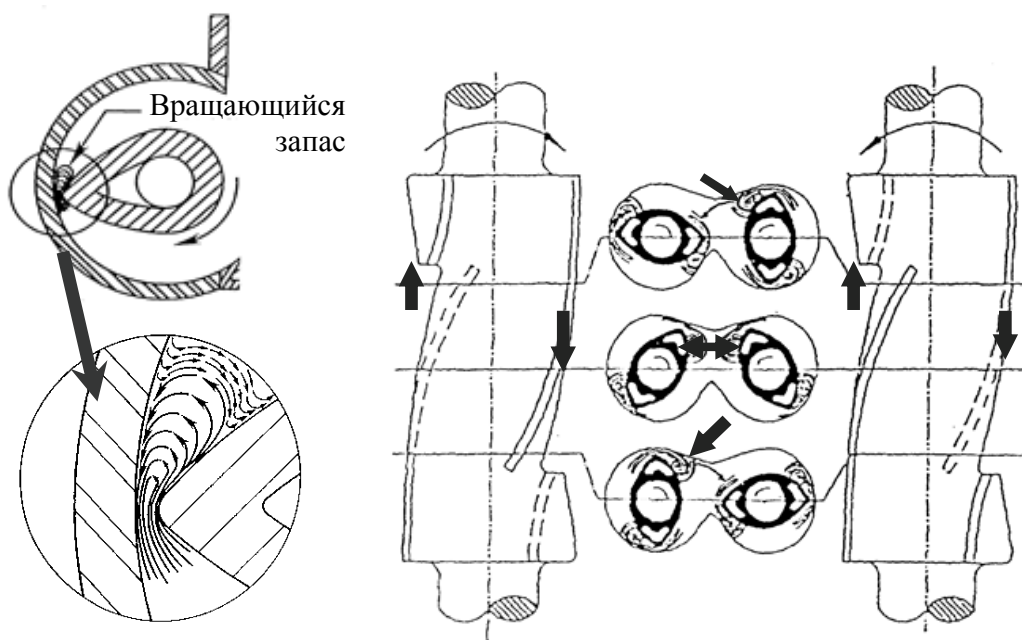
Схема обработки материала в резиносмесителях с тангенциальными роторами
